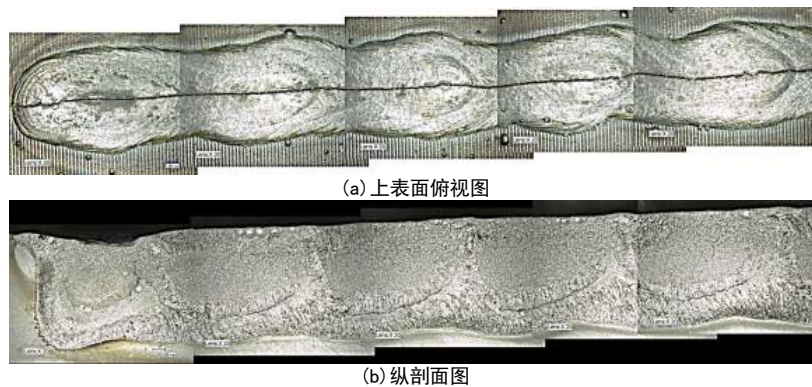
焊缝上表面和纵剖面的宏观形貌
